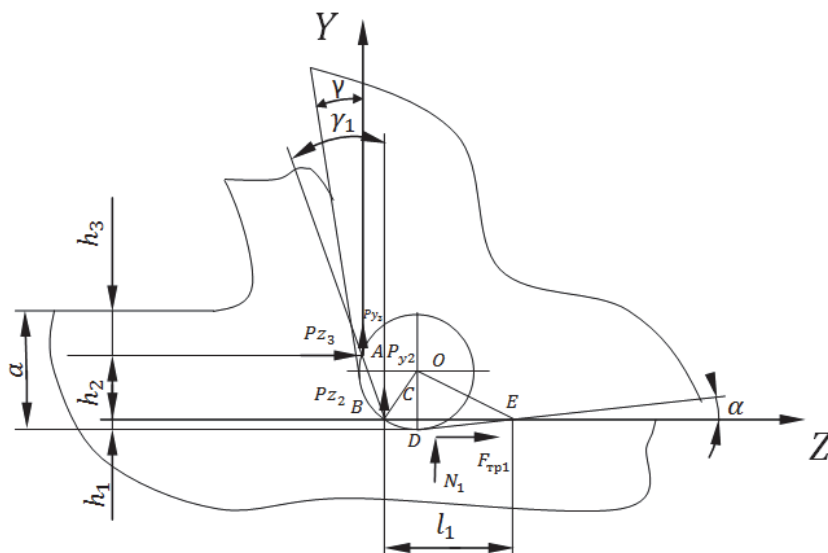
Распределение припуска тонколезвийной обработки для корундовой режущей пластины со скругленной режущей кромкой [2].
